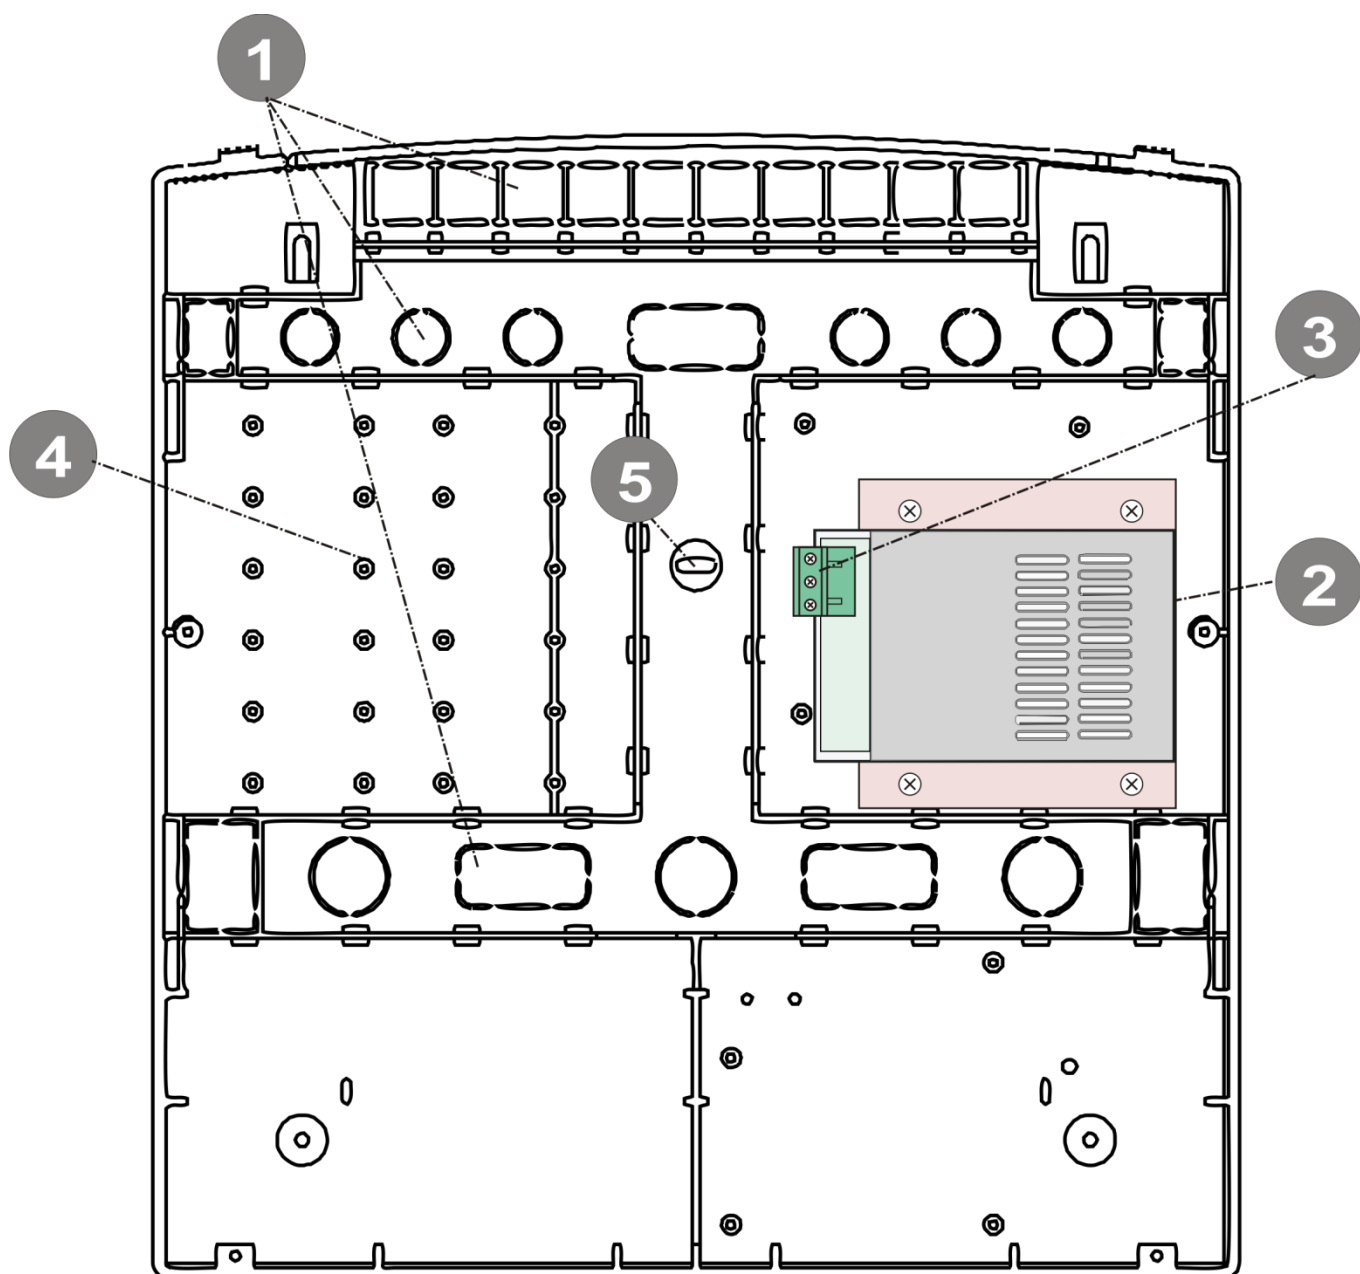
Внешний вид корпуса ППКП без основного модуля:
